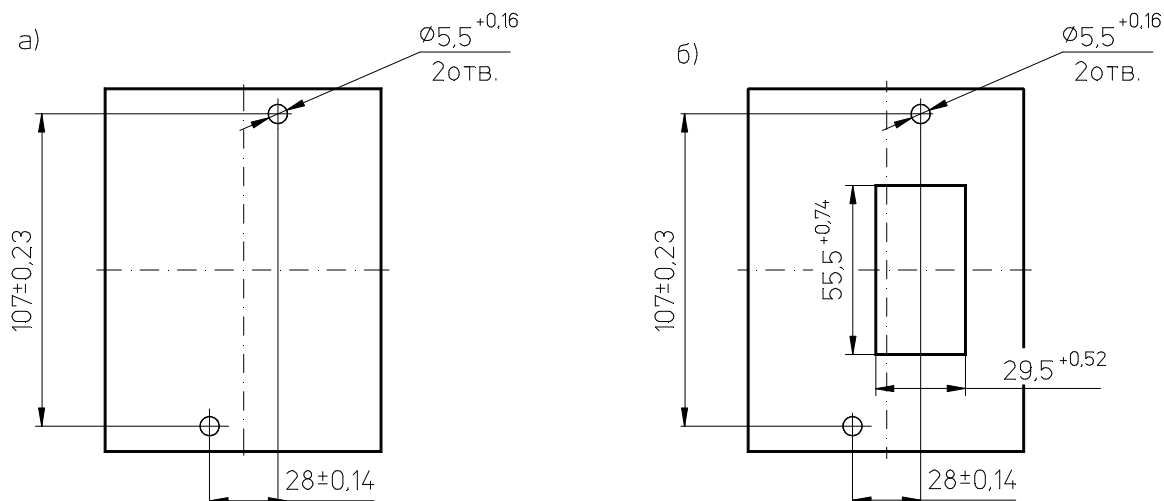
Сверление отверстий под винты крепления однополюсного выключателя в трехполюсном корпусе:
